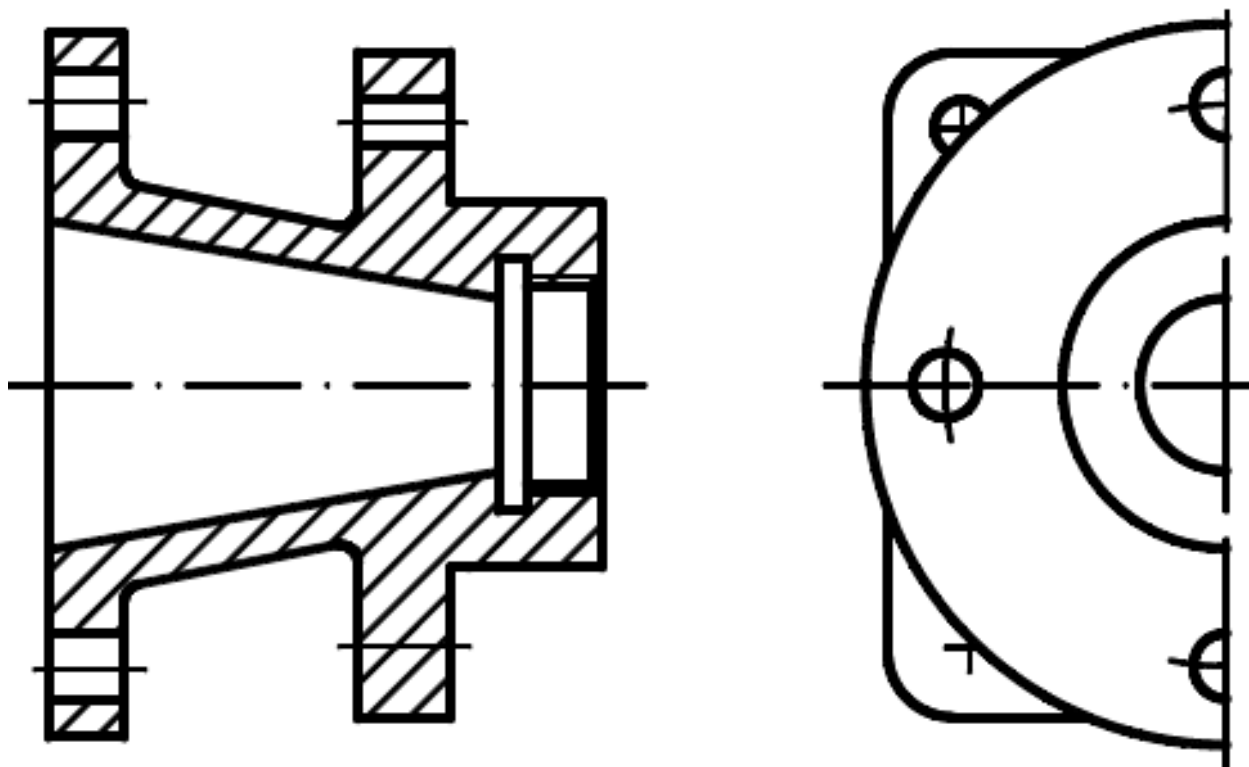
Второй этап выполнения рабочего чертежа детали по чертежу общего вида (детализирование)
